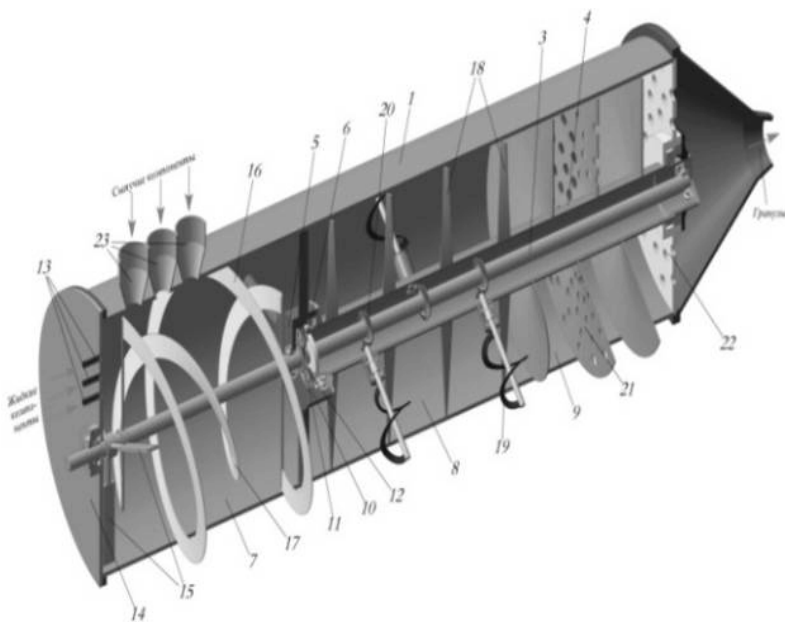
Общий вид смесителя – гранулятора: объемное изображение; 1 - корпус; 2 – загрузочный патрубок; 3 – быстроходный вал; 4 – тихоходный вал; 5 – опора; 6, 20 – зубчатое колесо; 7,8,9 – зоны; 10 – неподвижное колесо; 11 – водило; 12 – сателлит; 13 – форсунка; 14 – торцевая крышка; 15, 18 – лопасти; 16, 17, 19 – спирали; 21 – шнек; 22 – матрица; 23 – привод
